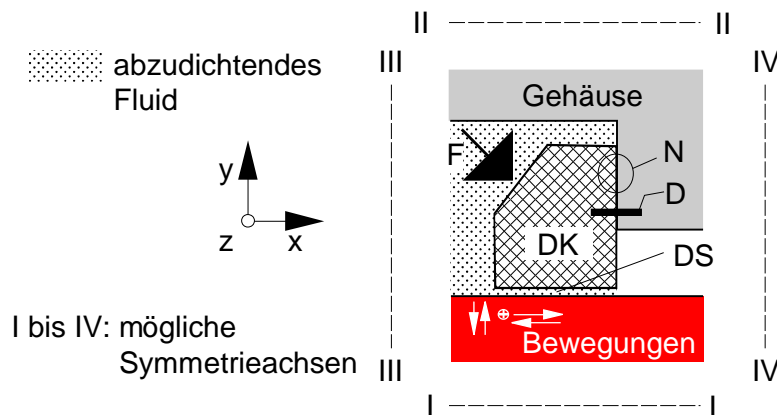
Grundelemente eines Dichtsystems nach /6-1/
